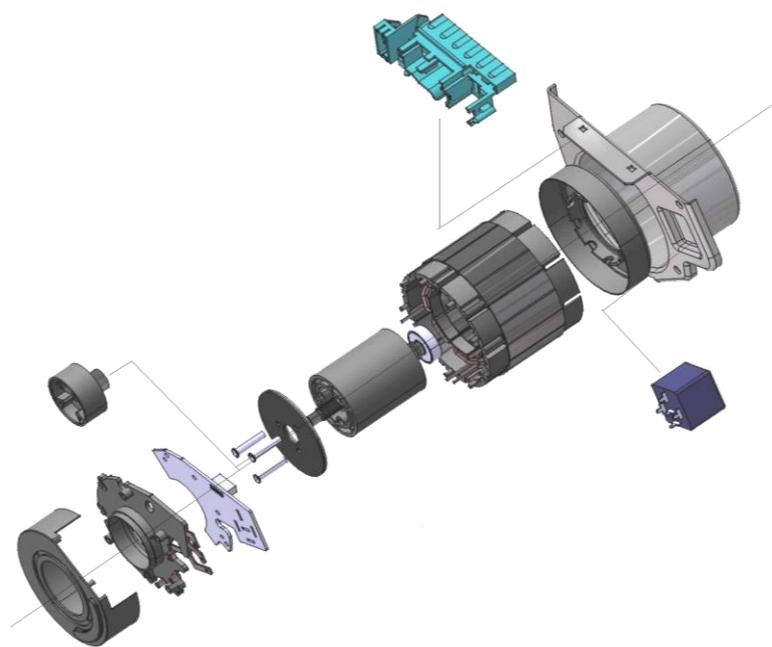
Despiece del Motor Eléctrico⁵⁸
